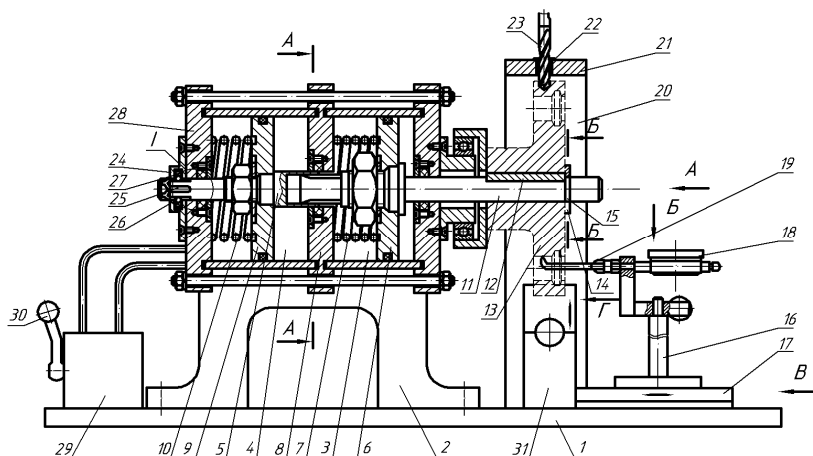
Універсальний пристрій для оброблення і контролю деталей
